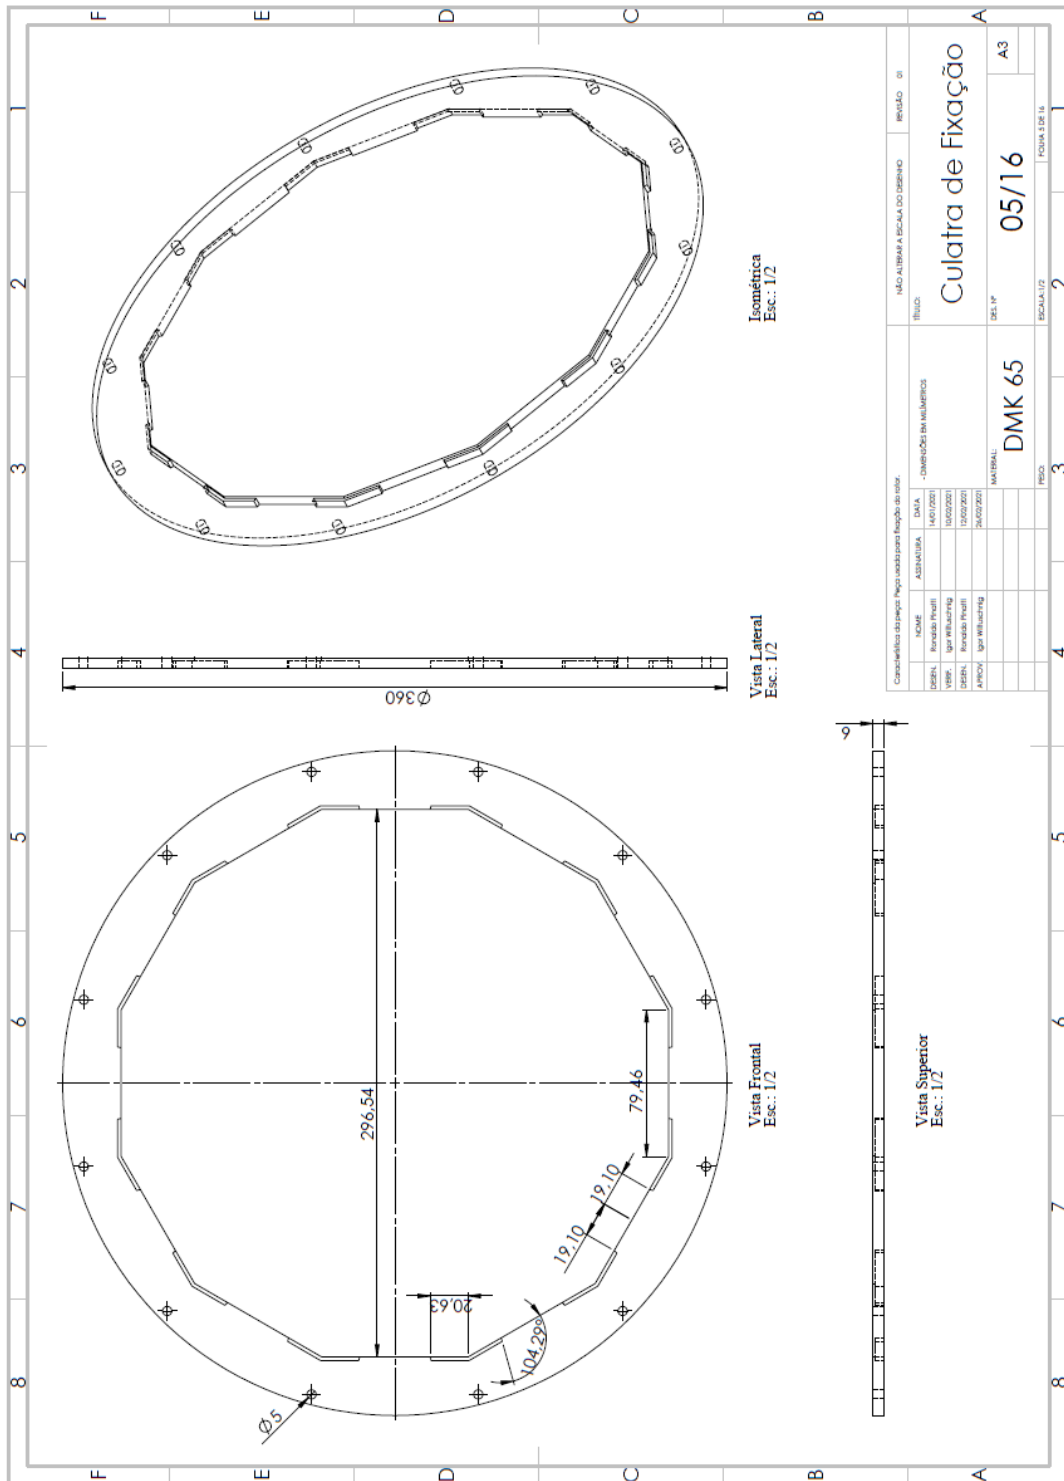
Desenho técnico do suporte (DMK65) do estator.
